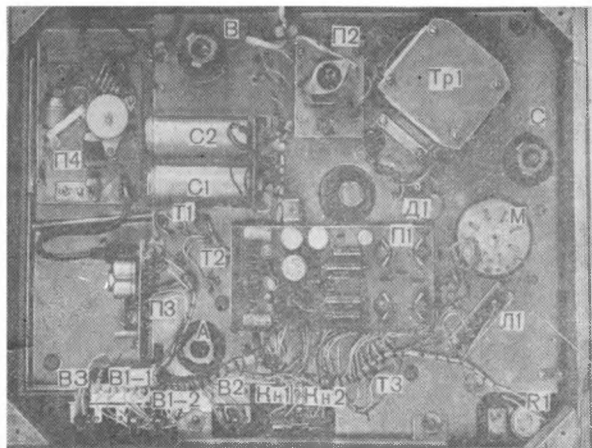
Вид проигрывателя снизу при снятой нижней крышке
